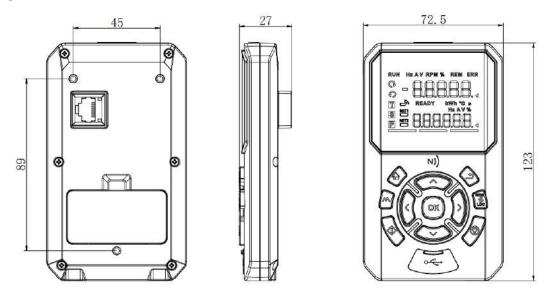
Внешний вид и монтажные размеры VT820-DP02 (в мм)
